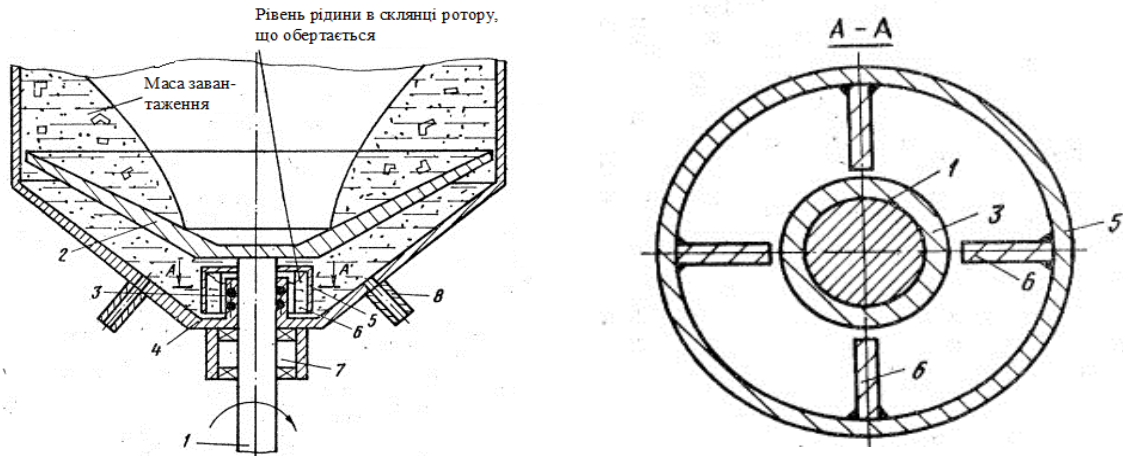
Пристрій для відцентрової обробки деталей малої маси:
